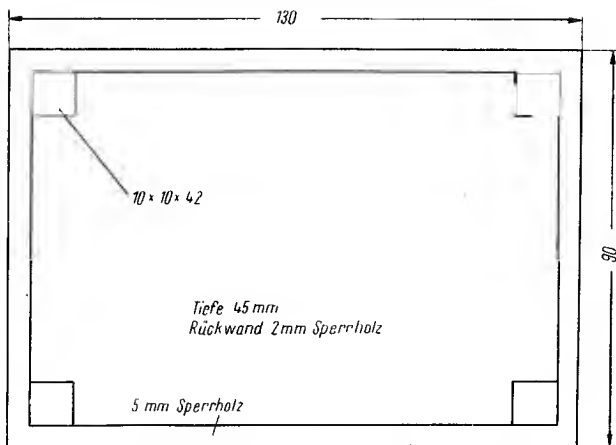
Maßskizze für das Holzgehäuse des Durchgangsprüfers
